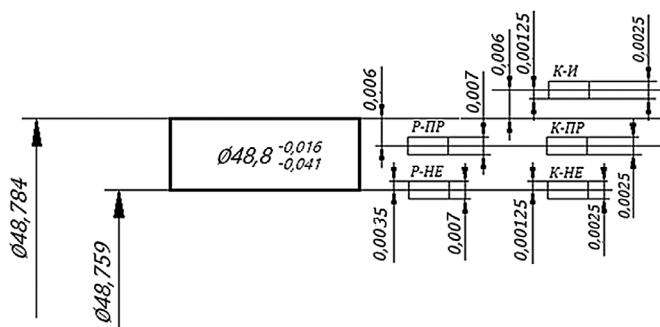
Схема расположения полей допусков калибра-скобы для контроля размера передней шейки промежуточного вала $\varnothing 48.8^{+0.016}_{-0.041}$ двигателей ЗМЗ
